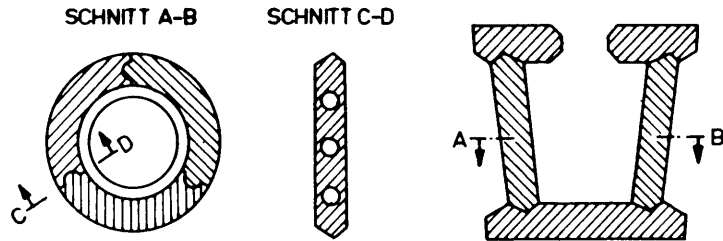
Schema einer Keil- oder Stückform (Gefäßform)
